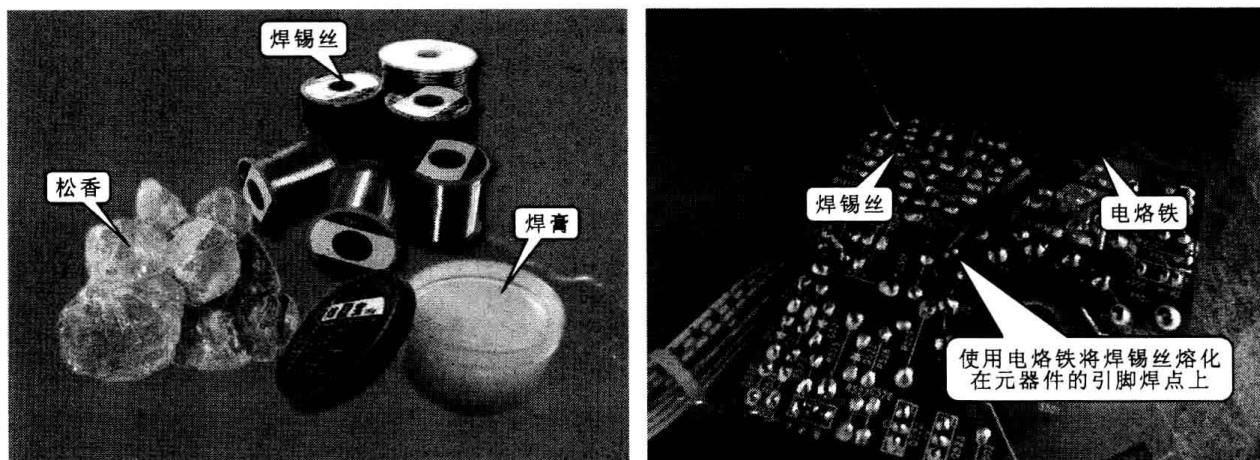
焊锡丝和助焊剂及使用方法
